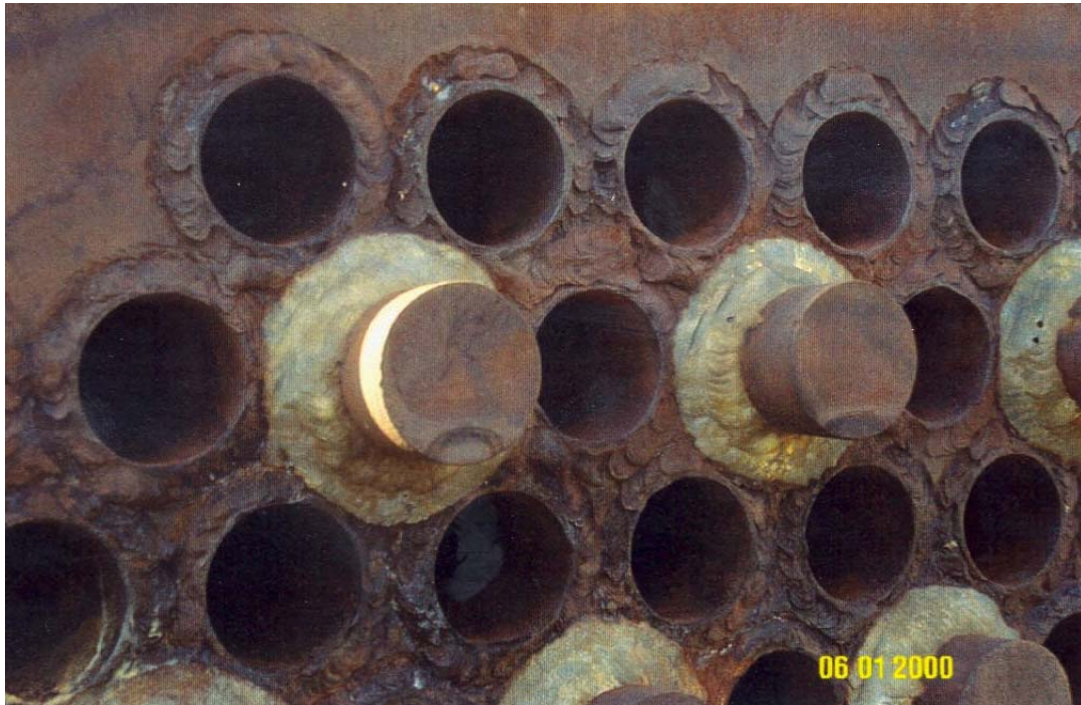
Corrosão nos cordões de solda de selagem dos tubos
